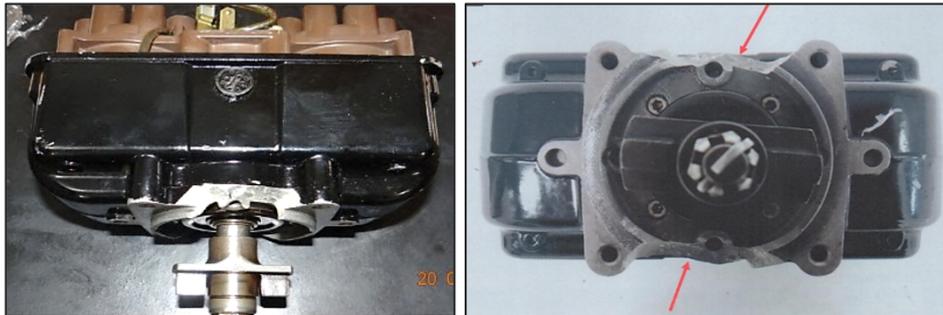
Vista geral do magneto duplo PN D8LN-3200 com os dois lados fraturados no seu flange de fixação.
